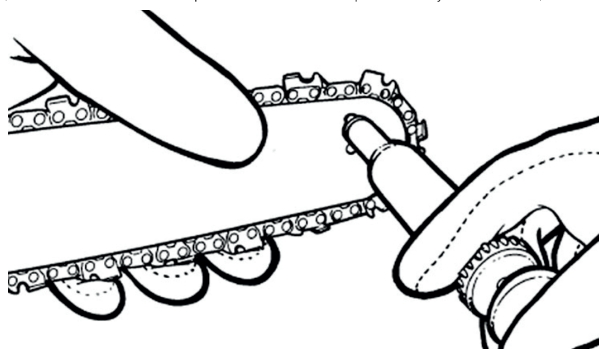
/ Fig. 18 Смазывание подшипника ведомой звездочки шины /
